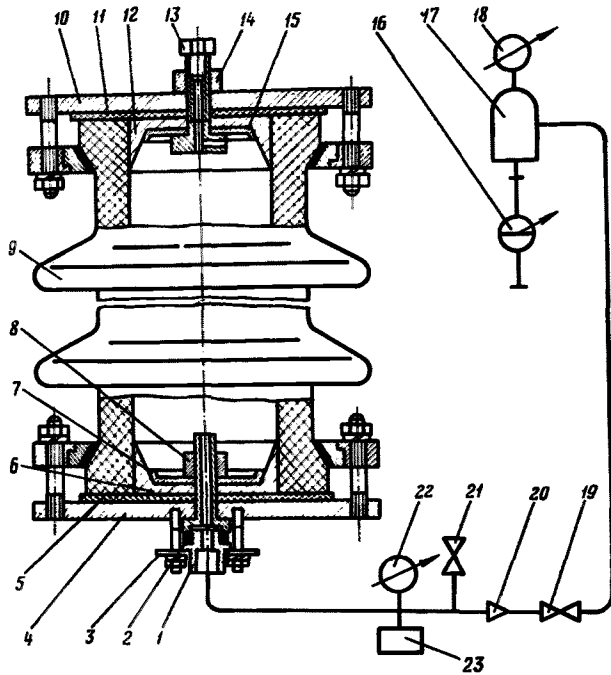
Схема установки для гидравлических испытаний изоляторов:
